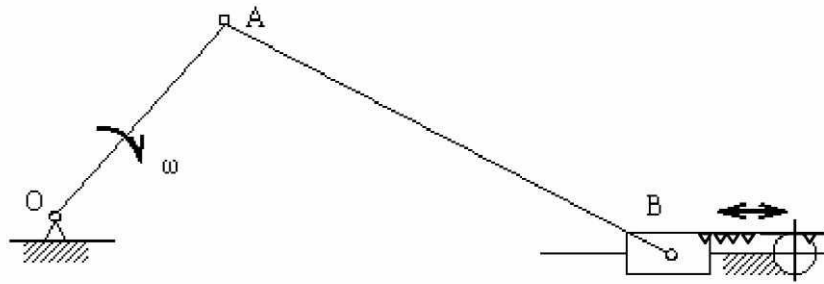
Кривошипно-ползунный привод ножовочного полотна
